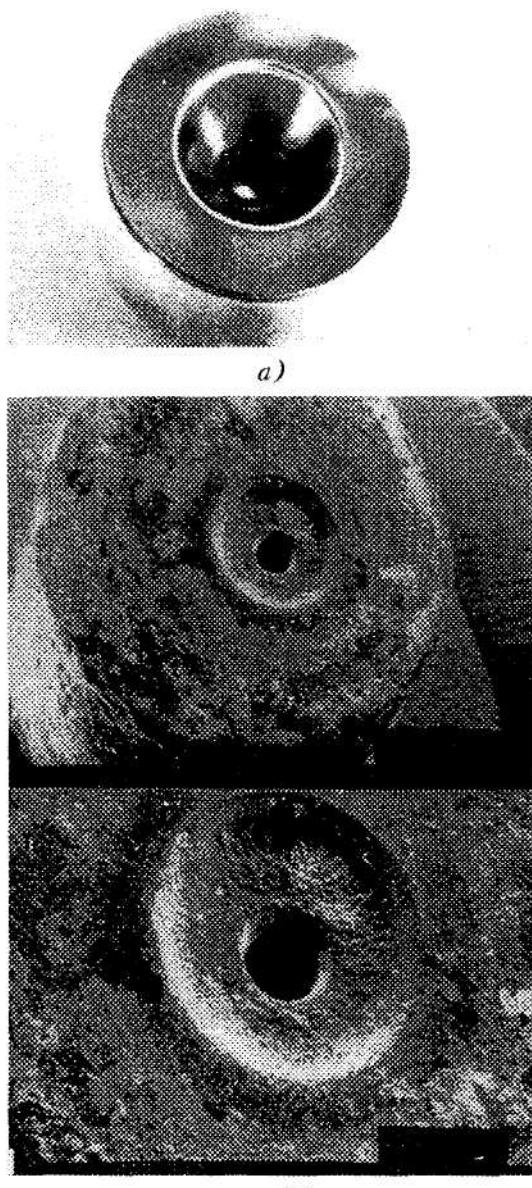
Вид вхідної частини отриманого лазерною обробкою профільного каналу:
